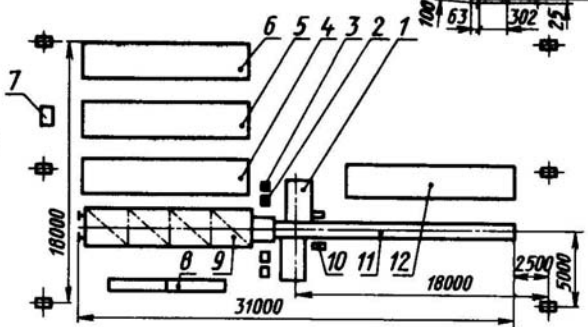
План механизированного участка контактно-дуговой точечной сварки
